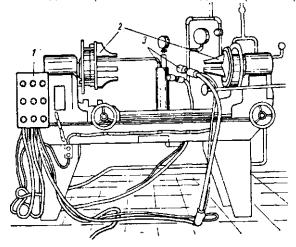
Сварочный станок A-320-01: 1 — пульт управлення; 2—неподвижная и подвижная бабки с трехкулачковыми патронами; 3—сварочные горелки.
